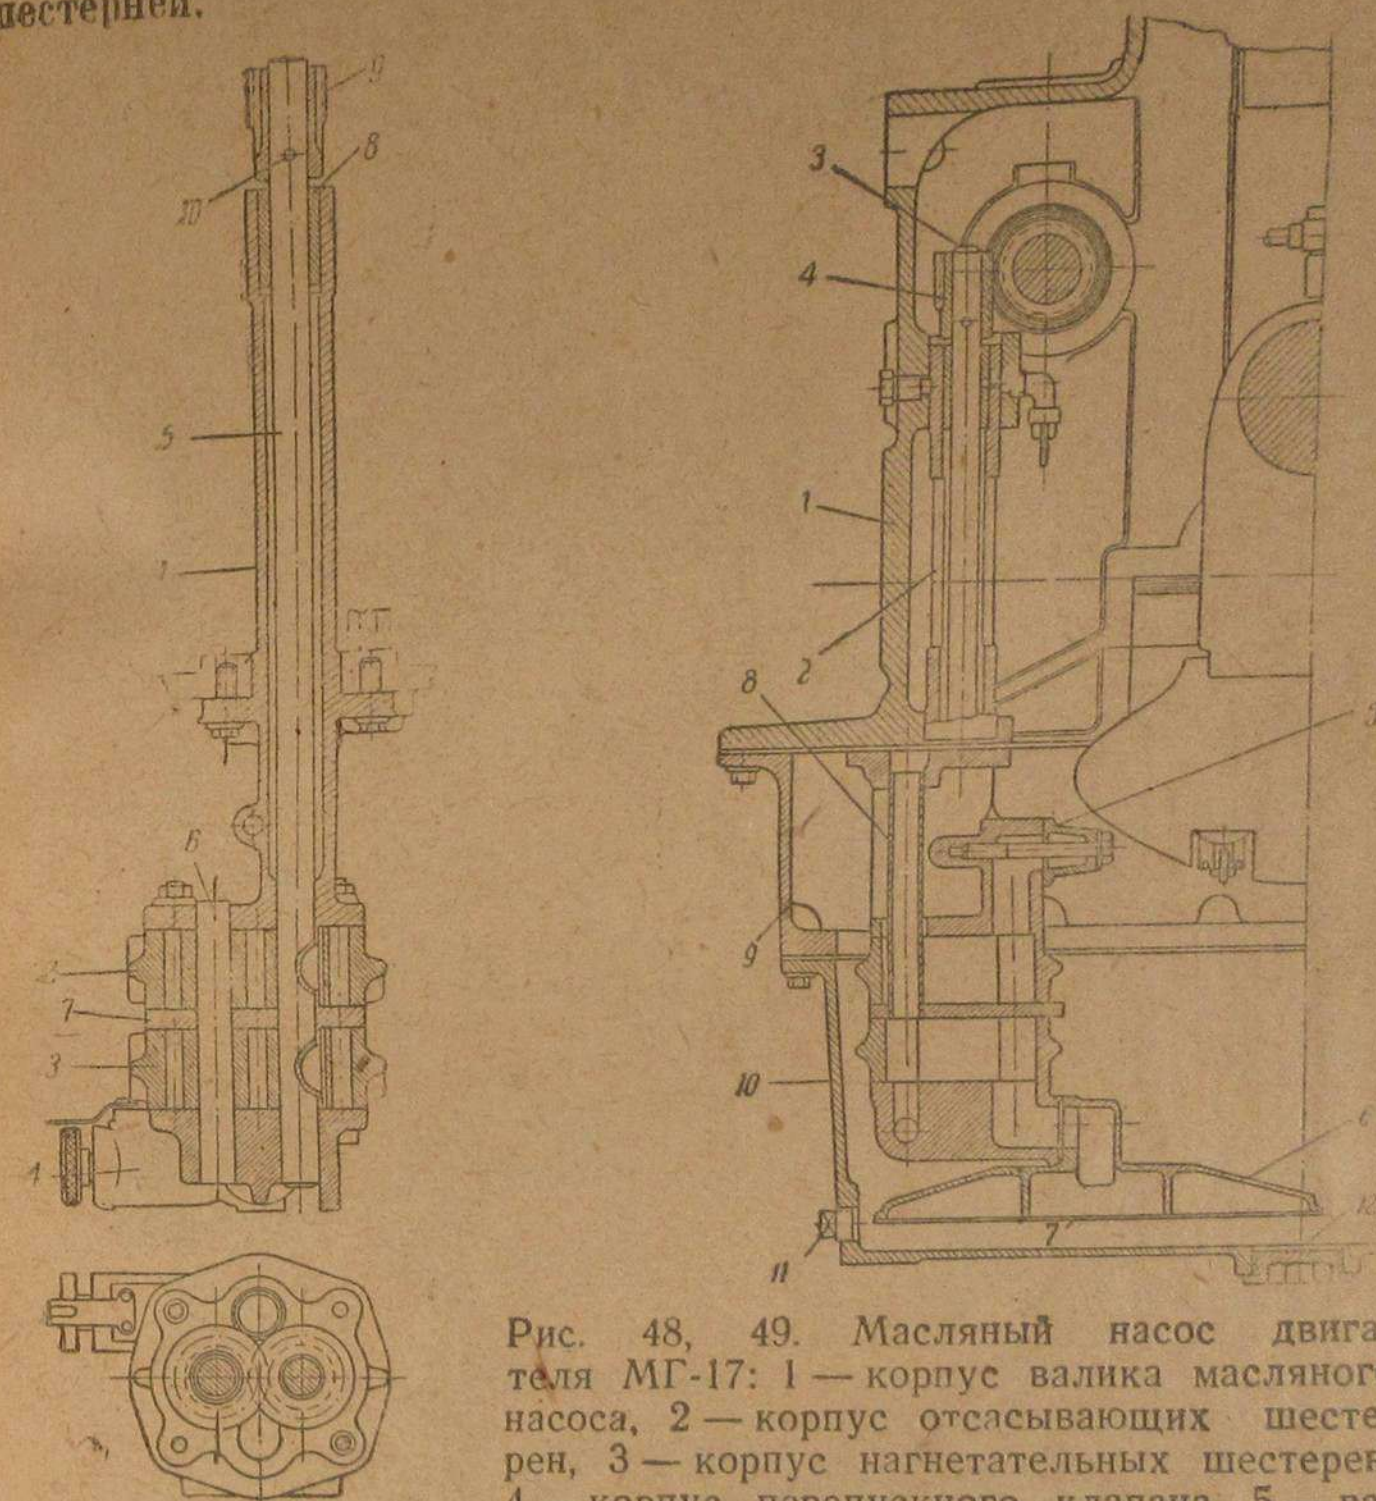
, 49. Масляный насос двигателя МГ-17: 1 — корпус валика масляного насоса, 2 — корпус отсасывающих шестерен, 3 — корпус нагнетательных шестерен, 4 — корпус перепускного клапана, 5 — валик масляного насоса, 6 — палец, 7 — отсасывающие шестерни, 8 — нагнетательные шестерни, 9 — плита, 10 — втулка корпуса валика масляного насоса, 11 — шестерня приводная, 12 — пробка
